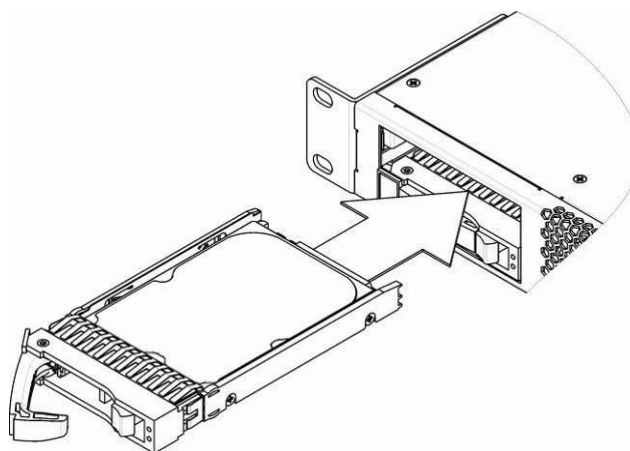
Монтаж SATA-диска в корпус устройства
